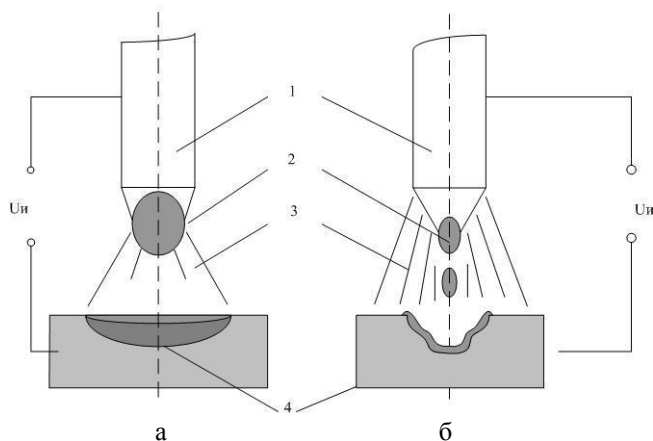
Разновидности переноса металла в дуге: а) крупнокапельный, б) мелкокапельный, 1- сварочная проволока; 2 - капля расплавленного металла; 3 - сварочная дуга; 4 - сварочная ванна.
